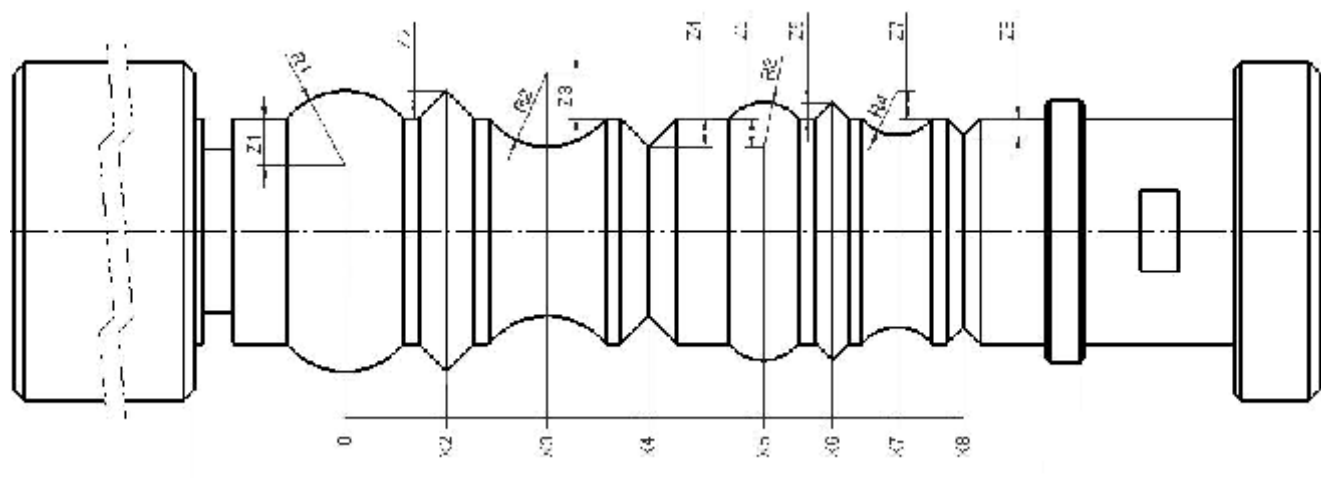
Схема мер для поверки приборов для измерений контура поверхности KN 100 S
